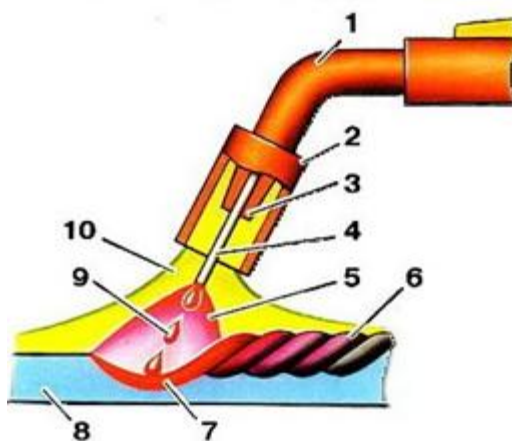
Схема полуавтоматической сварки в среде защитных газов:
